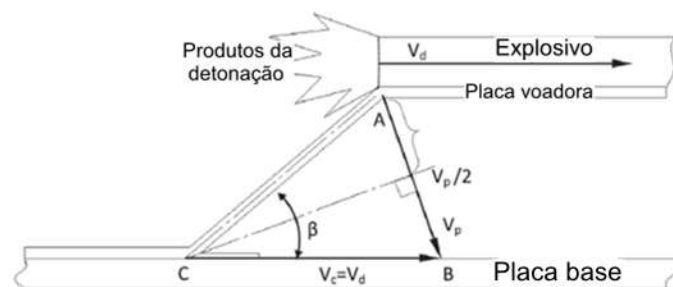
Representação esquemática do processo de soldagem por explosão (V_p), (V_d) e (β), adaptada de [9].
